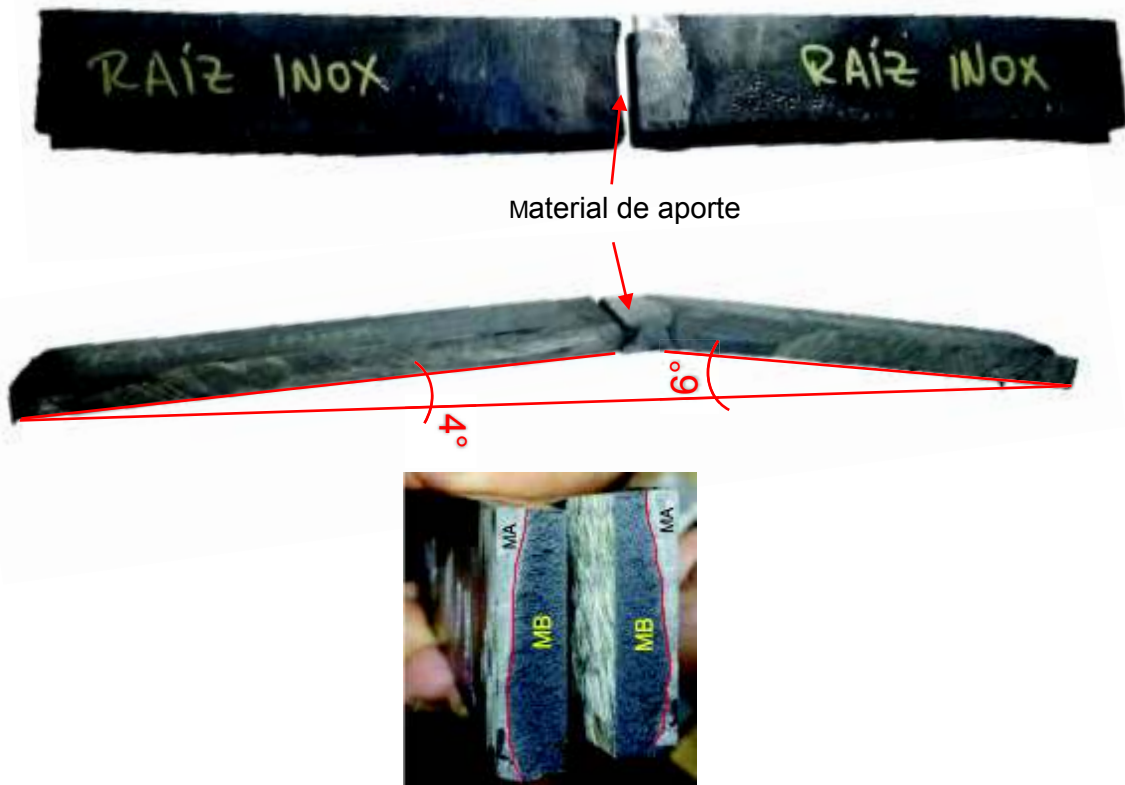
Doblado de raíz de la probeta soldada con M.A. AWS E 312-16.
